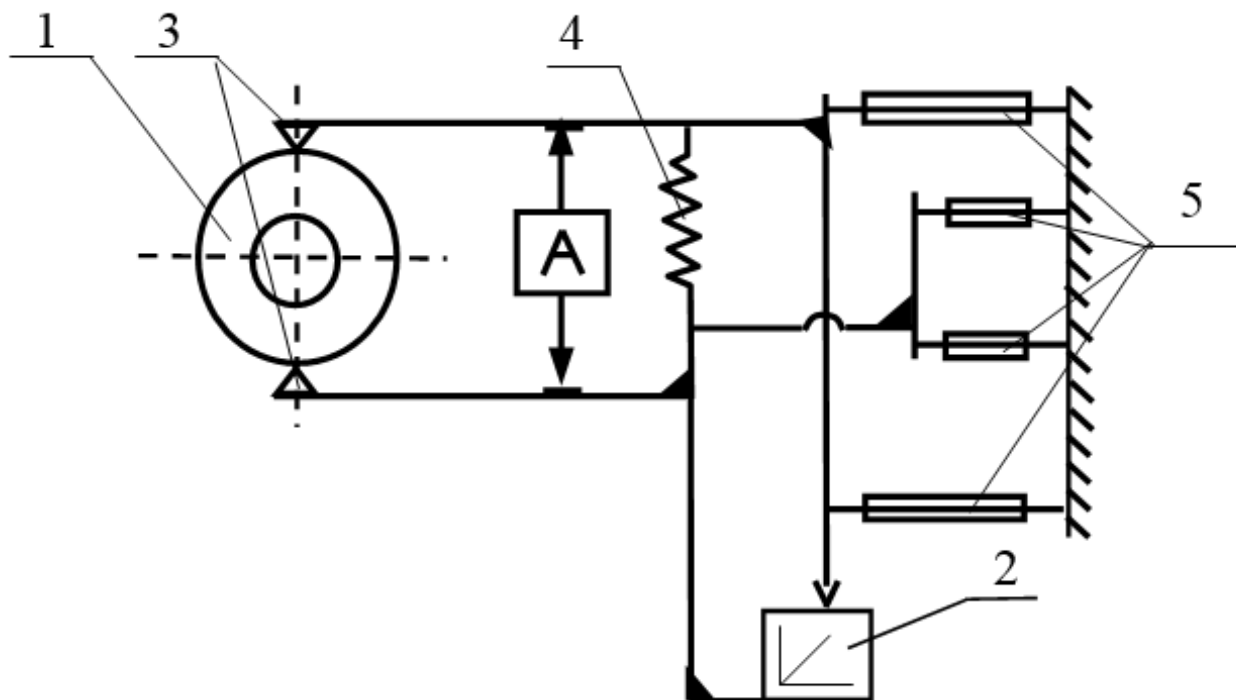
Вимірювальний пристрій для контролю зовнішнього діаметра деталі:
